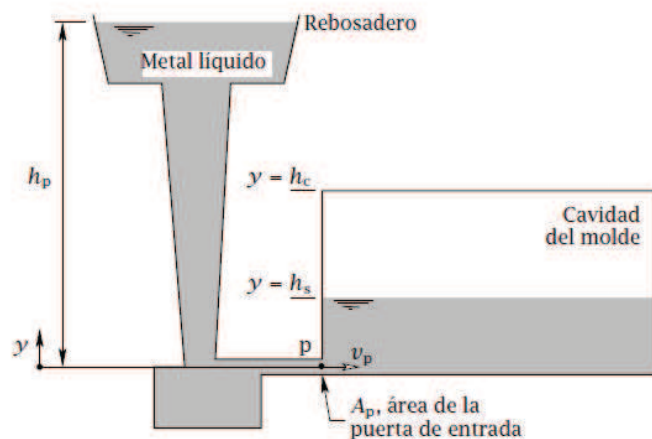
Llenado por la parte inferior de la cavidad del molde.
